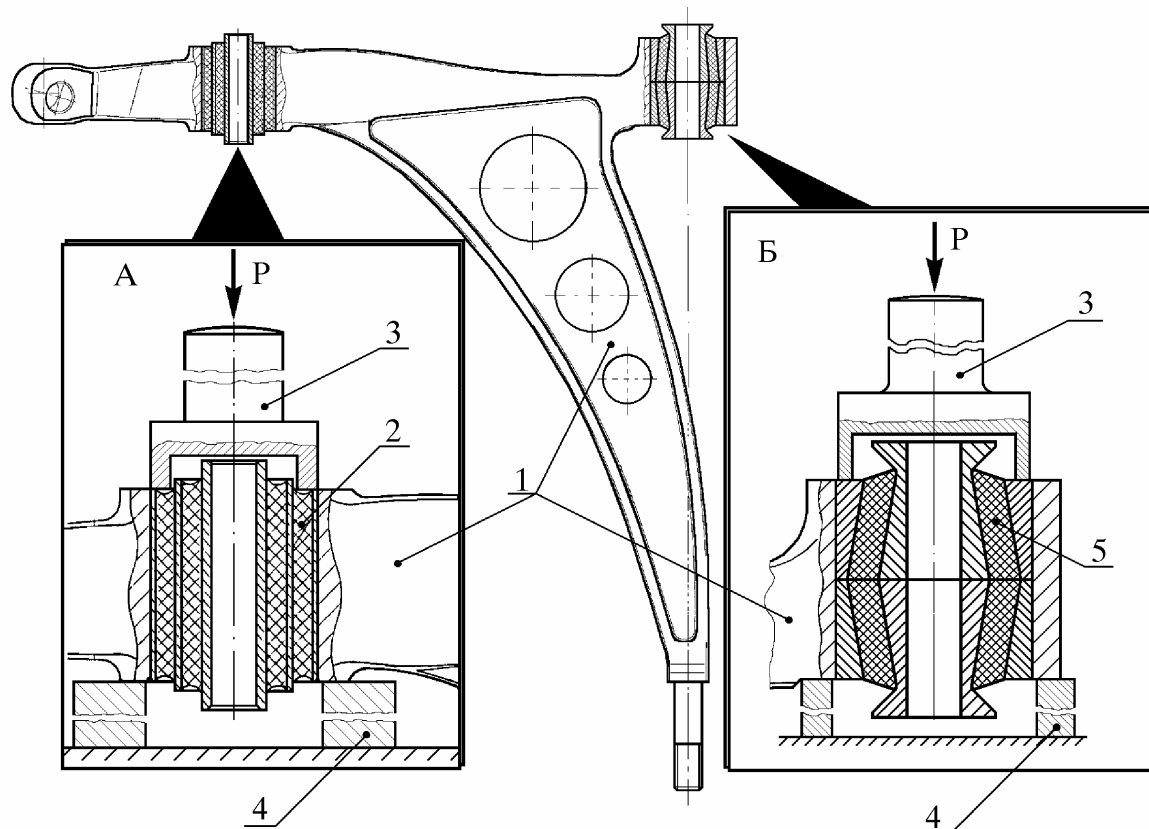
Выпрессовка шарнира амортизатора и сайлентблока из отверстий нижнего рычага:
